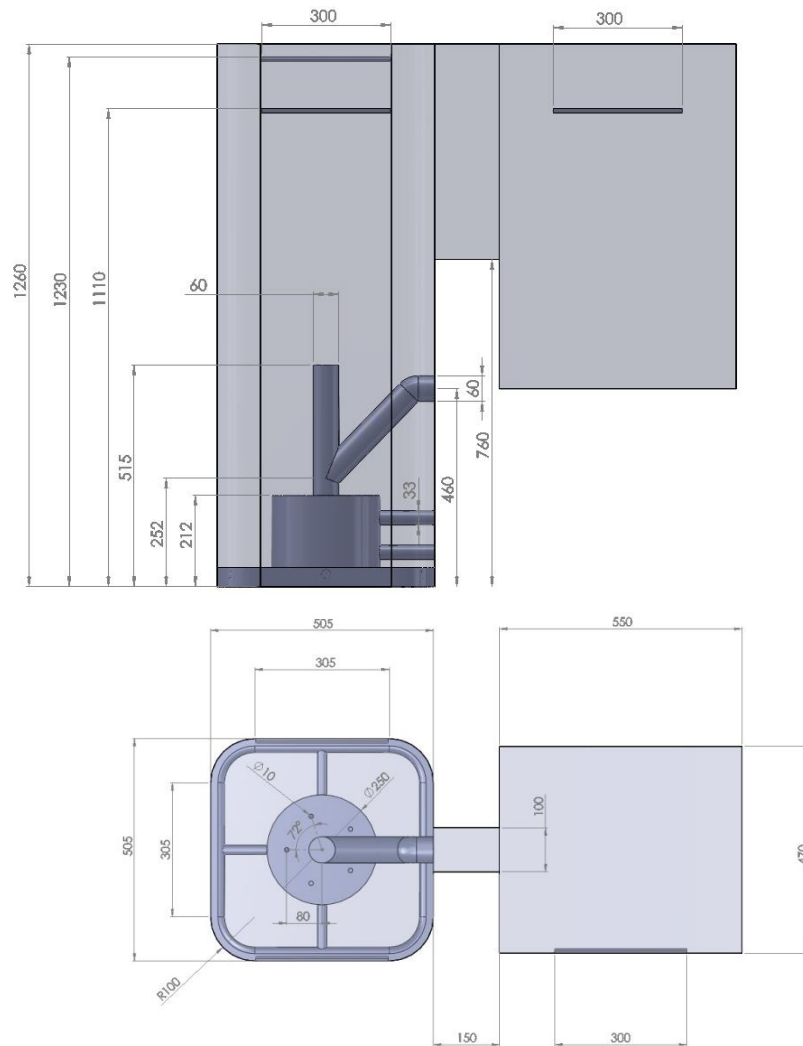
Vista de topo e elevação da geometria aplicada no modelo do experimento.
